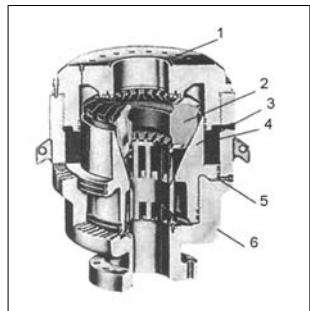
Універсальний превентор тину ГК (компанія „Hydri”): 1 – гвинтова кришка корпусу; 2 – ущільнювач; 3 – плунжер; 4 – камера відкриття; 5 – камера закриття; 6 – корпус.
